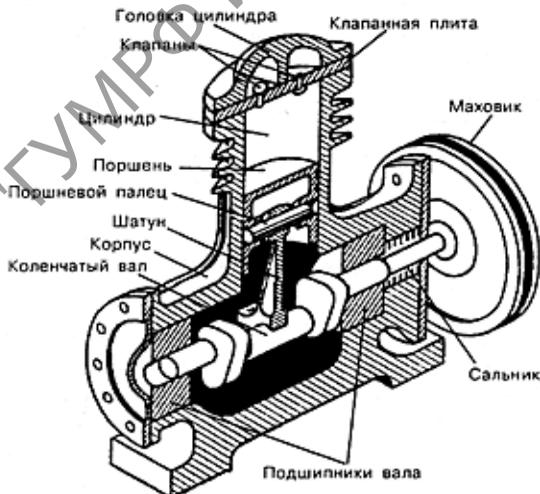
Детали простейшей конструкции поршневого компрессора
